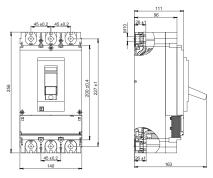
Габаритные, установочные и присоединительные размеры выключателей
